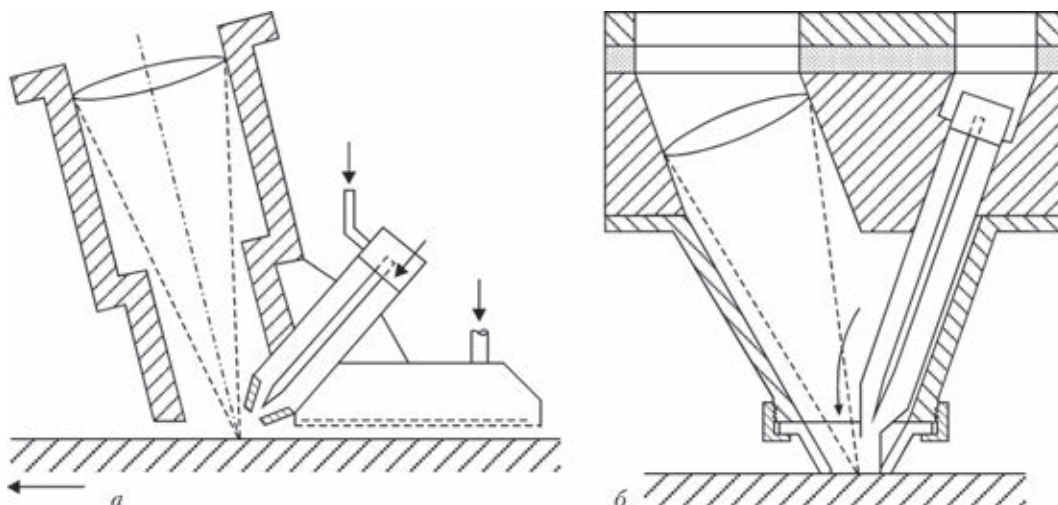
Конструкции гибридных лазерно-плазменных сварочных головок, в которых лазерная фокусирующая система и плазменная горелка используются раздельно (а) либо интегрируются в общий корпус (б) [13]
